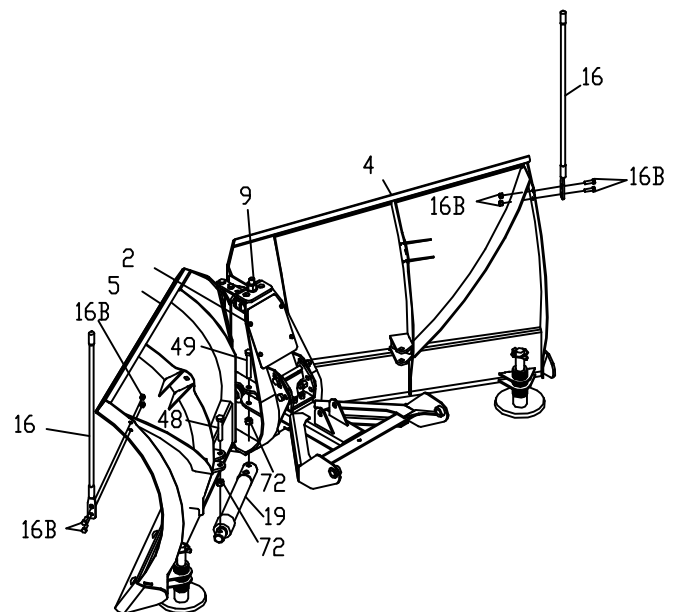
Zylinder und Pflugbegrenzer Montage G10627
